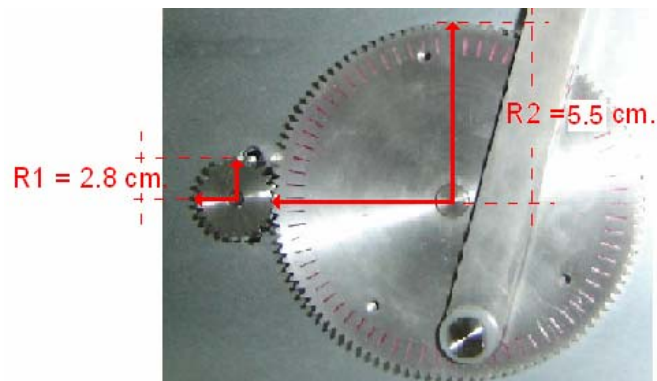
DIMENSIONES DE LOS ENGRANES
